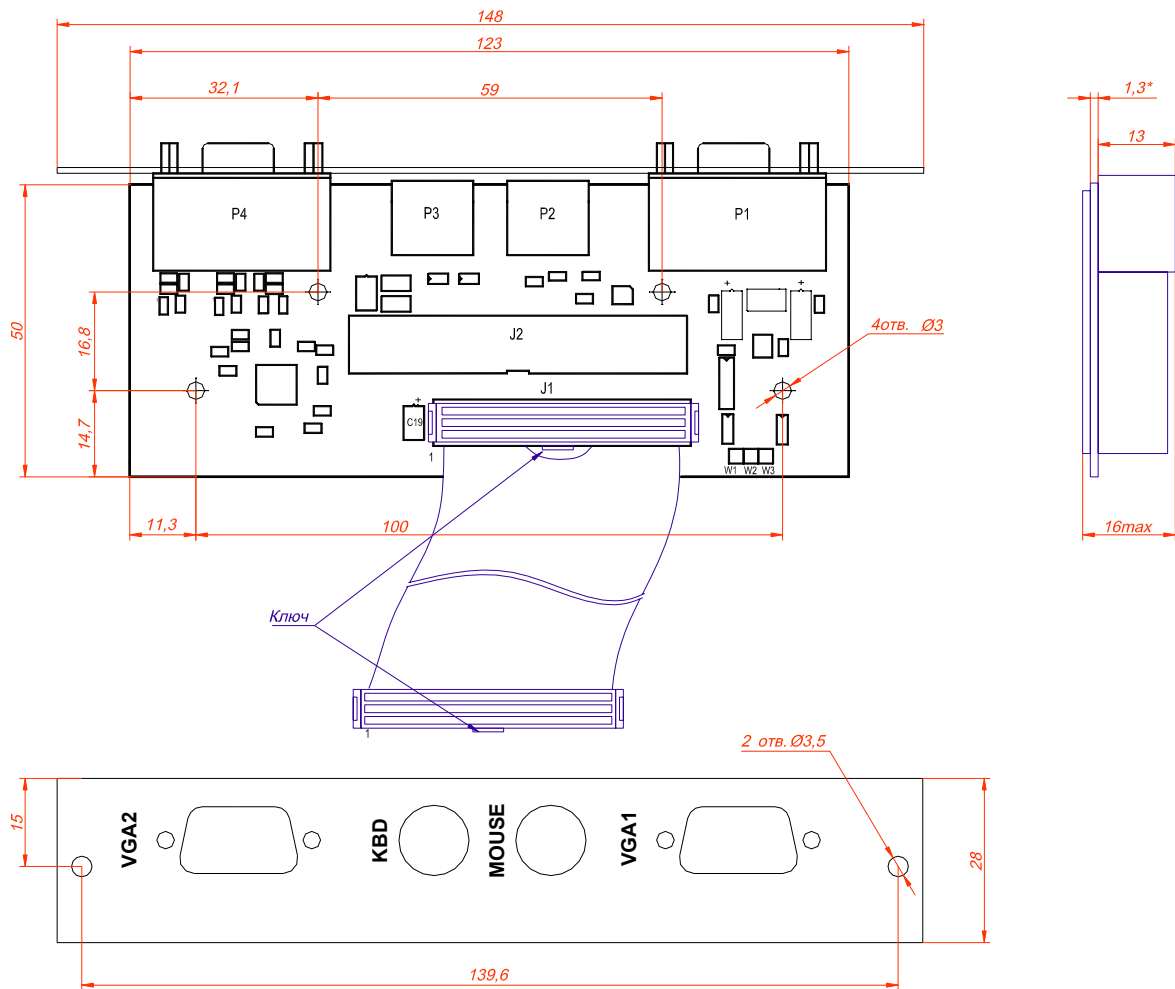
Габаритные и присоединительные размеры интерфейсного модуля CUM01
